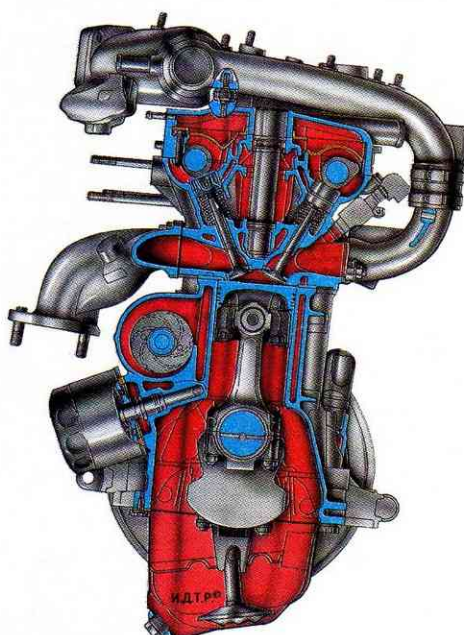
Поперечный разрез двигателя ВАЗ-2112
